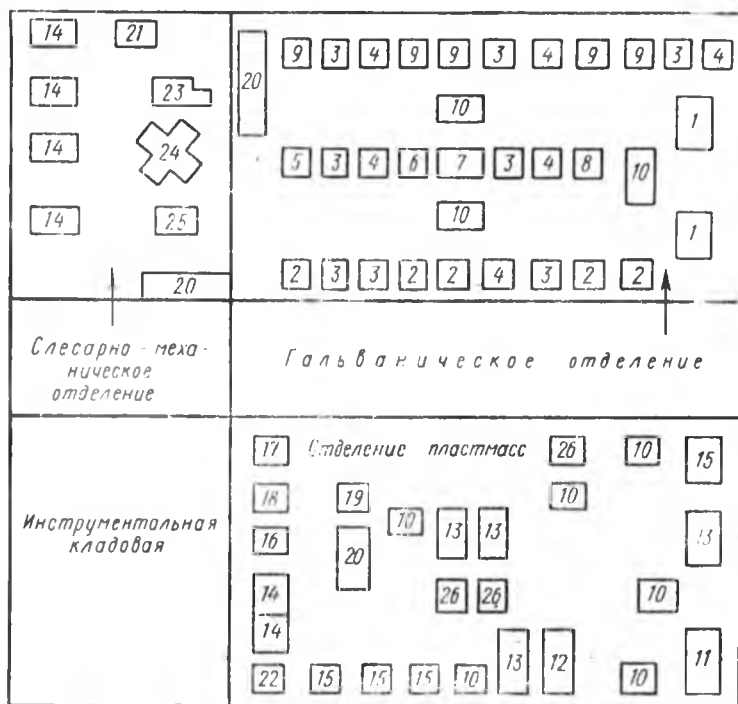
Планировка участка для изготовления волноводных корпусов гальванопластическим методом с последующей опрессовкой:
